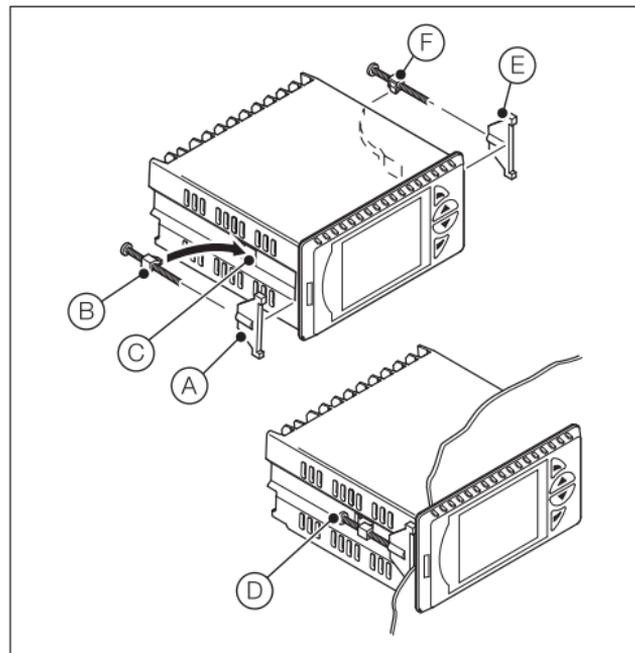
Dettagli di montaggio – Indicatore CM15
